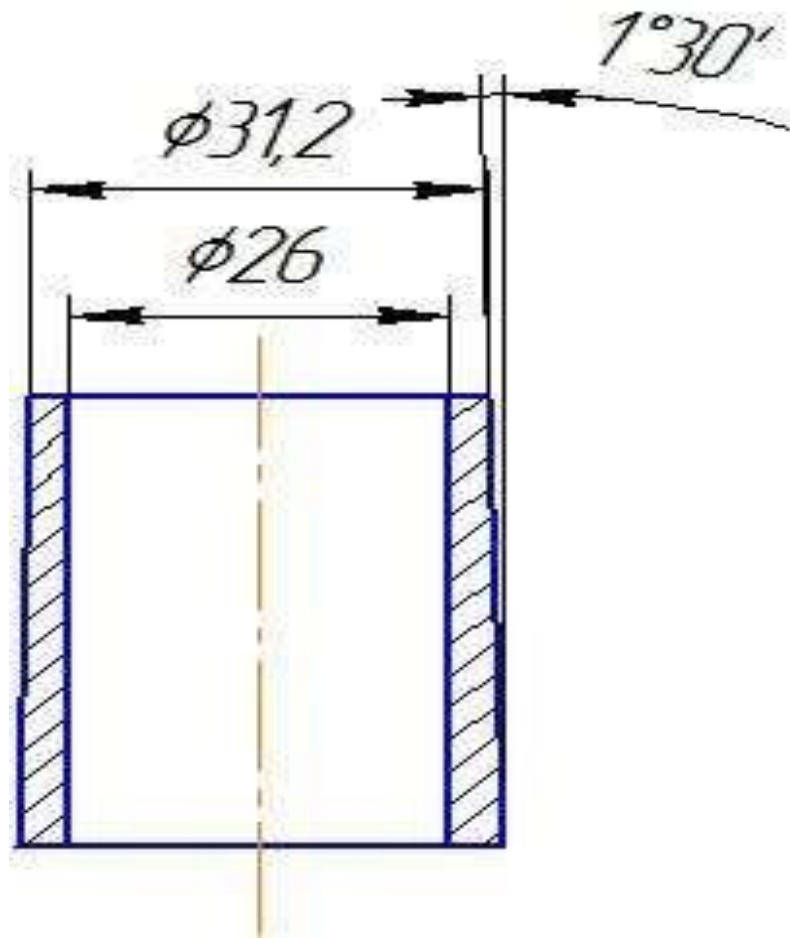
Ескіз матриці для зворотного видавлювання
